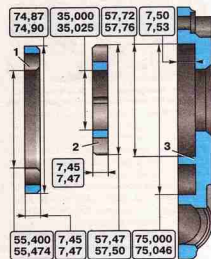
Основные размеры деталей масляного насоса: 1 – ведомая шестерня; 2 – ведущая шестерня; 3 – клапан
